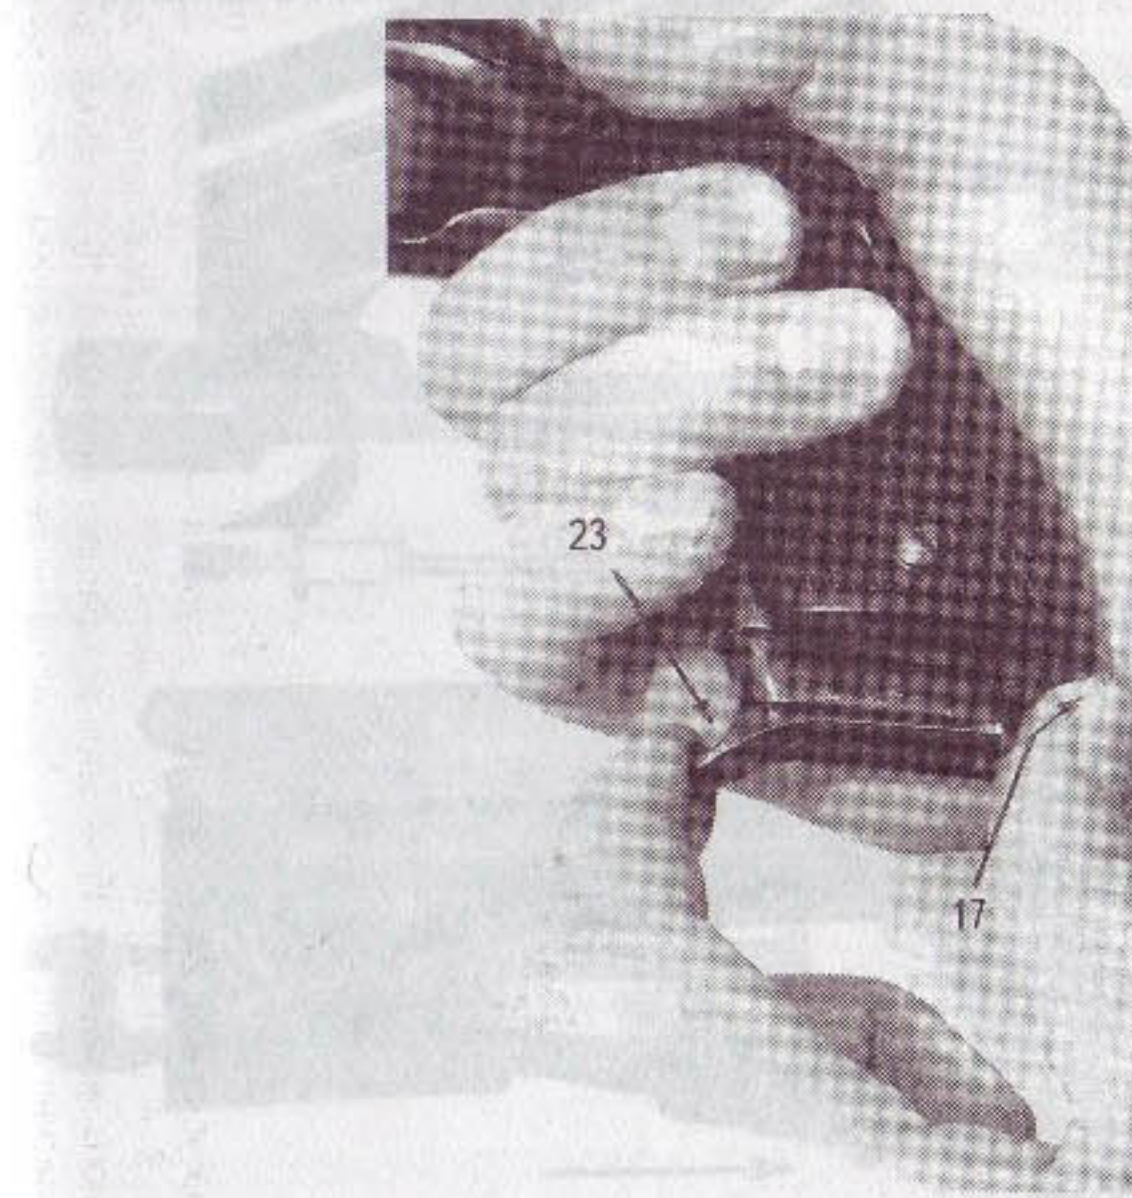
Разборка пистолета: сдвинуть назад защелку магазина (17); извлечь из рукоятки магазин (23)
